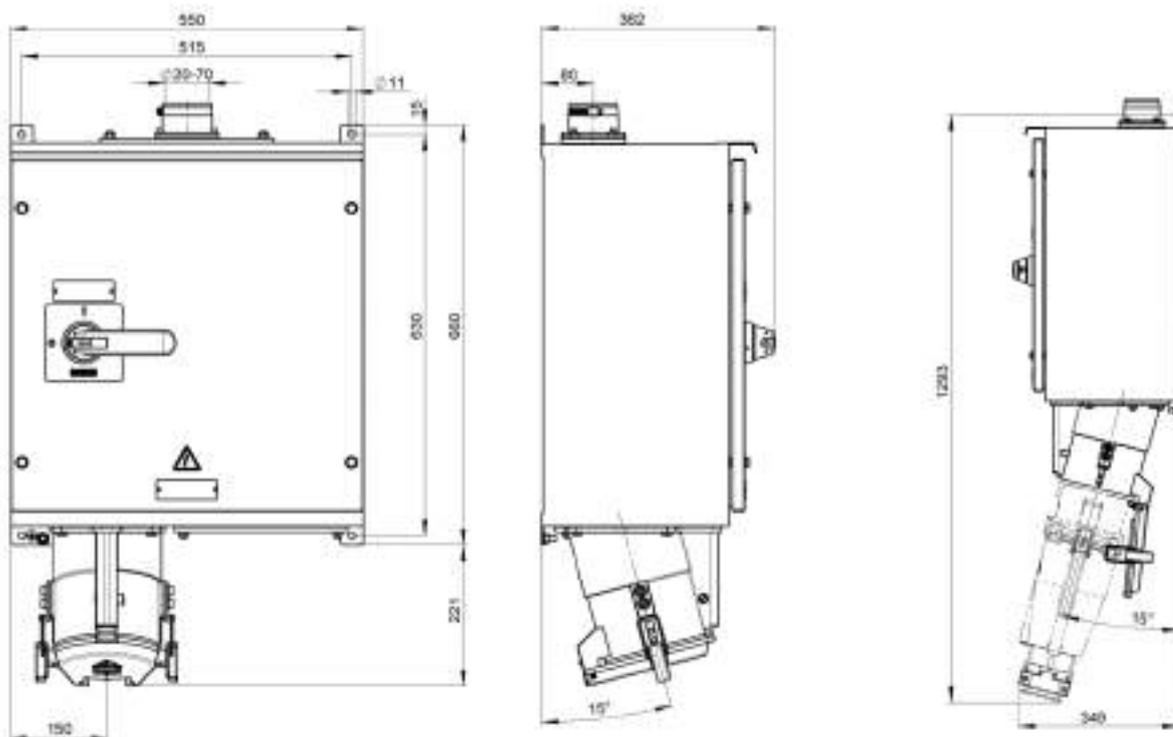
Abmessungen Anschlusskasten mechanisch verriegelt CUMI B-Line, A-Line (250 A – 600 A) in mm
